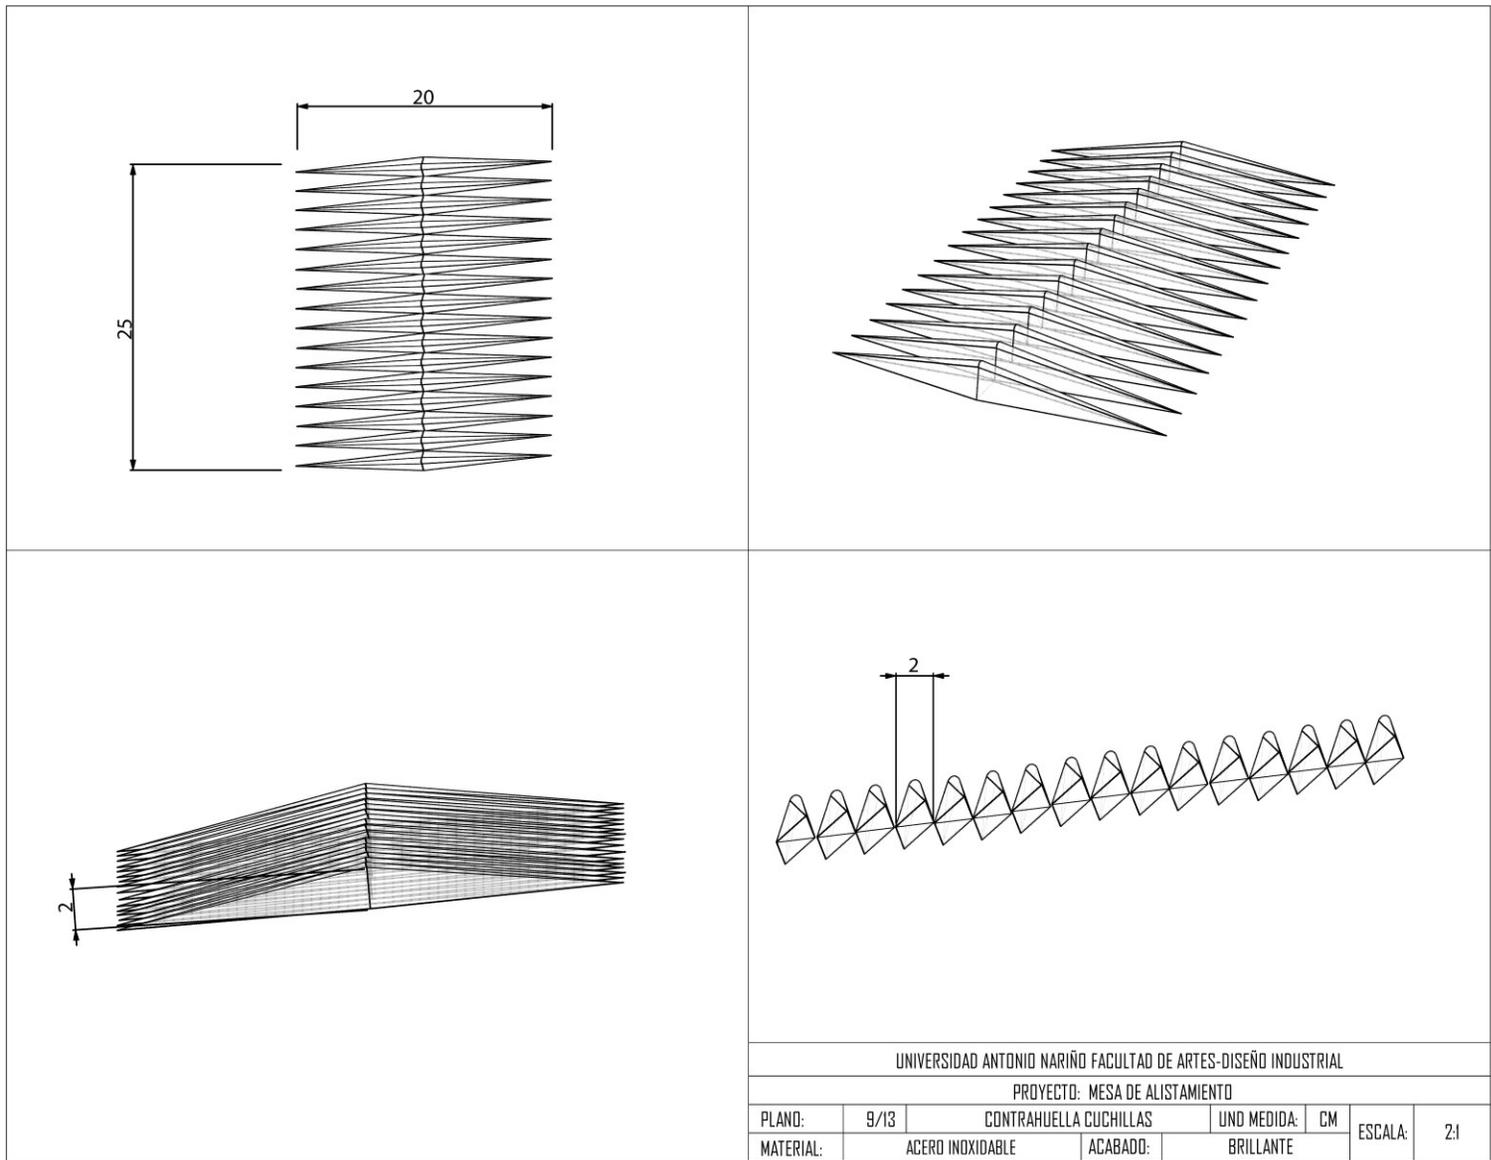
Planos piezas 8 (Elaboración propia, 2020)
